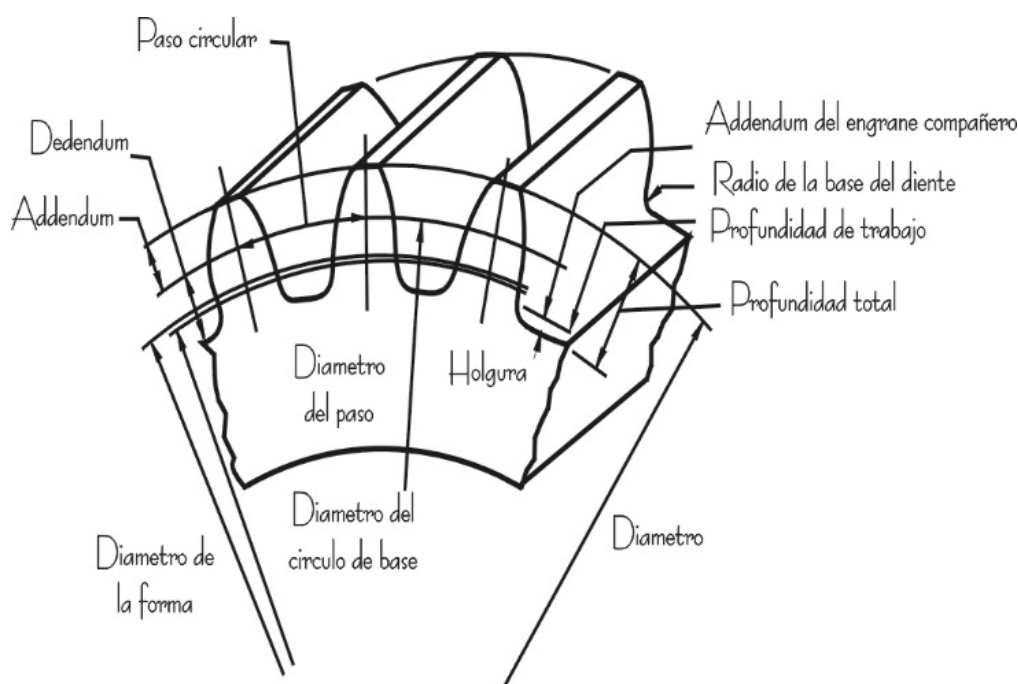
Engranaje cilíndrico de dientes rectos.
